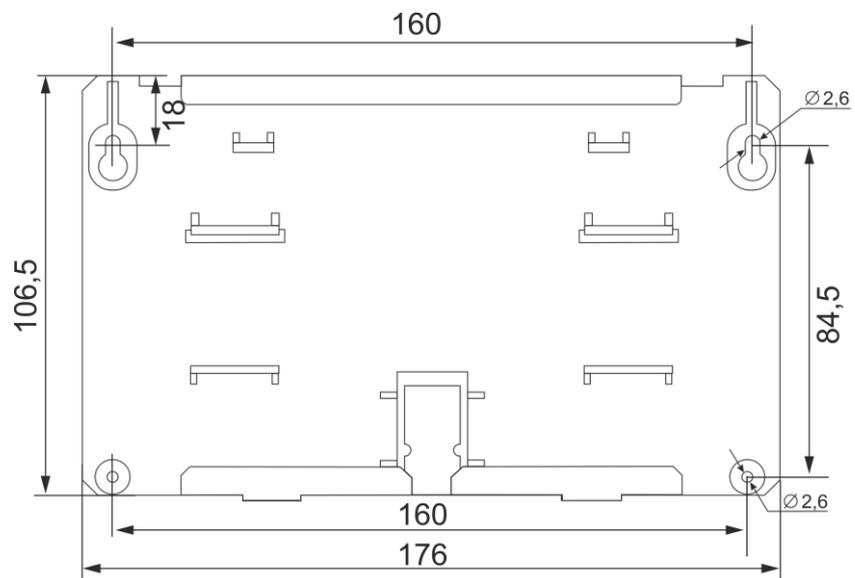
Установочный чертеж основания корпуса ПИУ-А24Б
